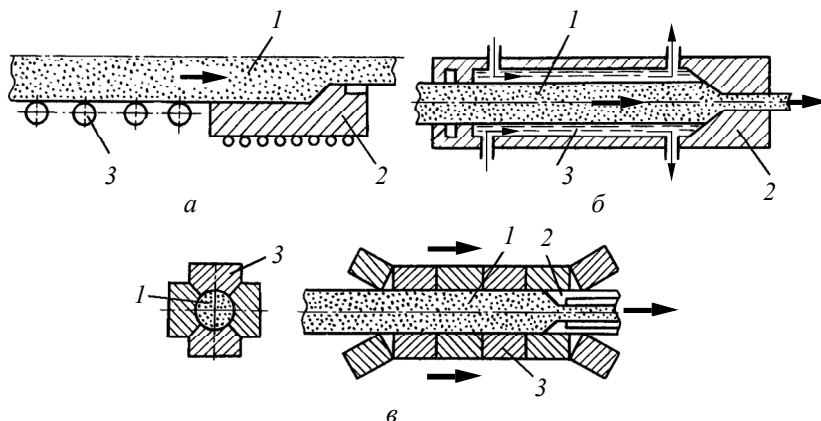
Схемы непрерывного прессования с использованием различных способов (а–в) подачи заготовки:
